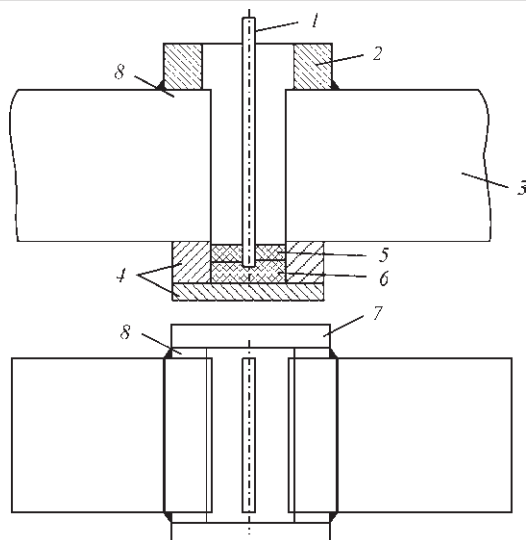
Схема ЭШС: 1 — пластинчатый электрод; 2 — выводящие планки; 3 — свариваемый стык; 4 — металлический карман; 5 — рабочий флюс; 6 — экзотермическая смесь; 7 — формирующие подкладки; 8 — боковые планки
